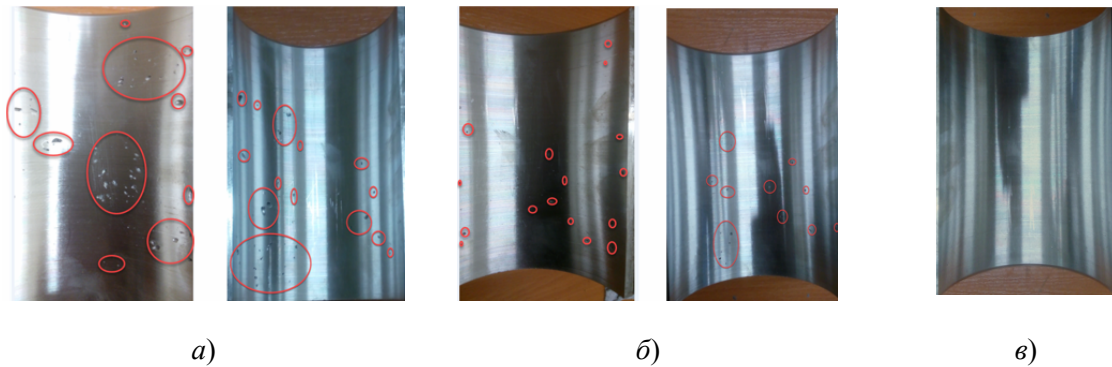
Внутренняя поверхность образцов отливок при различной газопроницаемости образцов литейного стержня:
